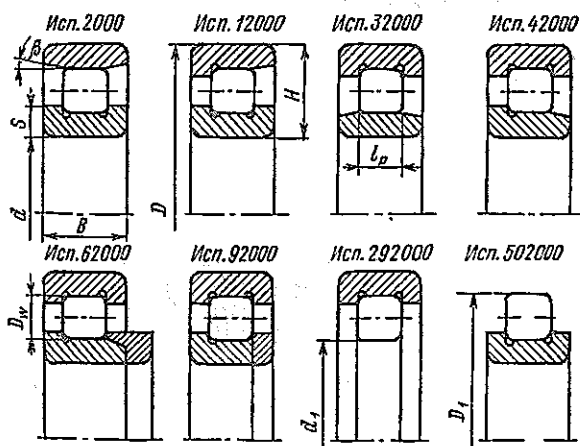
Радиальные подшипники с короткими цилиндрическими роликами типа 2000
